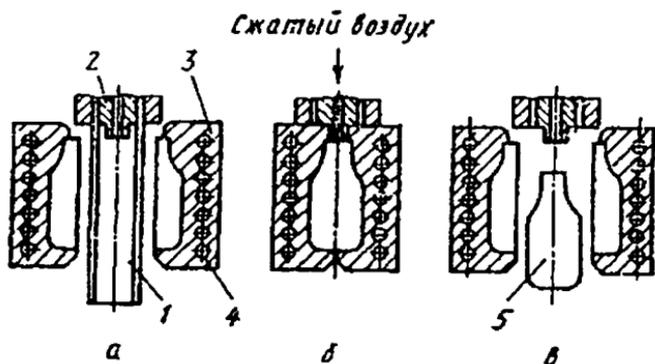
Схема раздувки полых изделий: а — форма разомкнута и подана заготовка; б — форма сомкнута и подан сжатый воздух; в — форма разомкнута; 1 — трубчатая заготовка; 2 — головка экструдера; 3 — форма; 4 — каналы для охлаждения формы; 5 — изделие
